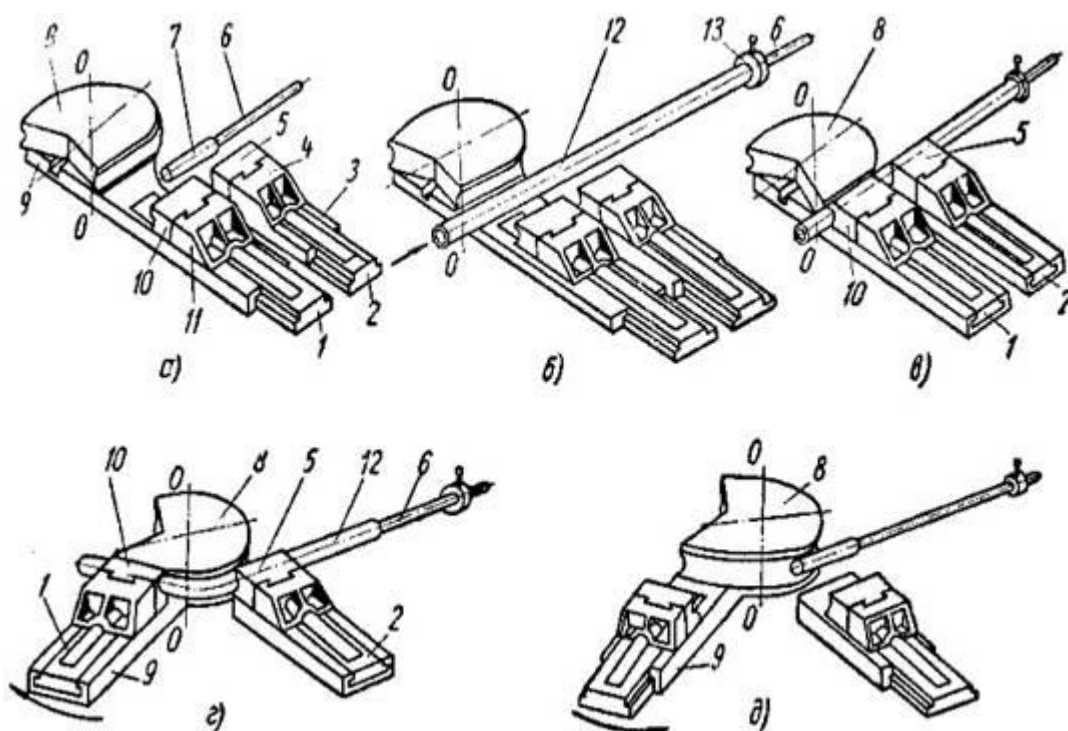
Цикл гибки труб: а) подготовка станка к загрузке трубой, б) загрузка станка трубой, в) начало гибки трубы, г) гибкиа трубы, д) возвращение станка в исходное положение. 1-суппорт, 2-суппорт, 3-планка, 4-упор, 5-вкладыш, 6-стержень, 7-дорн, 8-гибочный сектор, 9-поворотный стол, 10-вкладыш, 11-упор, 12-труба
